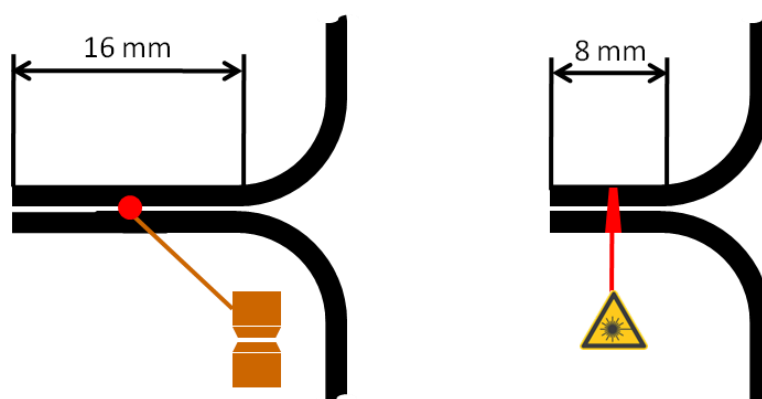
Сравнение ширины фланца точечной сварки сопротивлением (слева) и фланца, сваренного лазерным лучом
